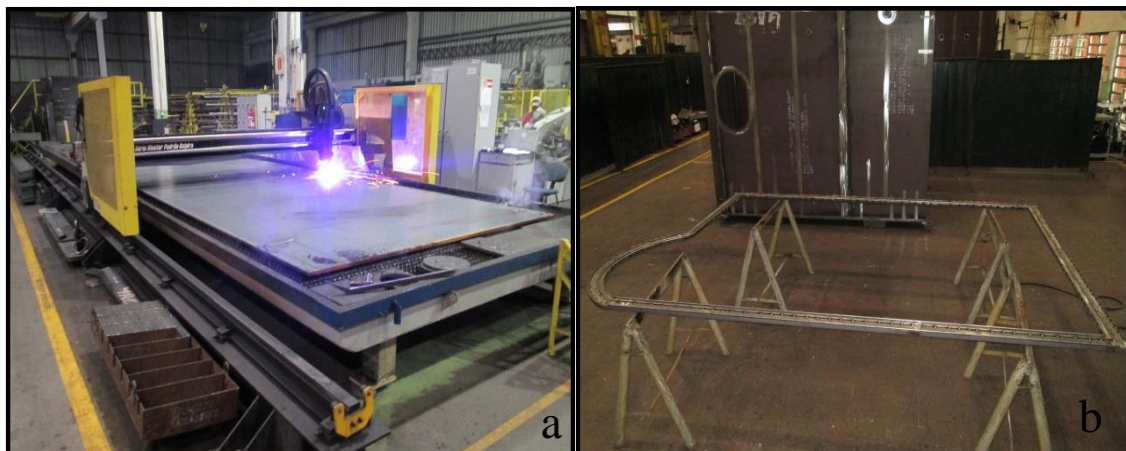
Corte Plasma e 4b montar e soldar o flange
